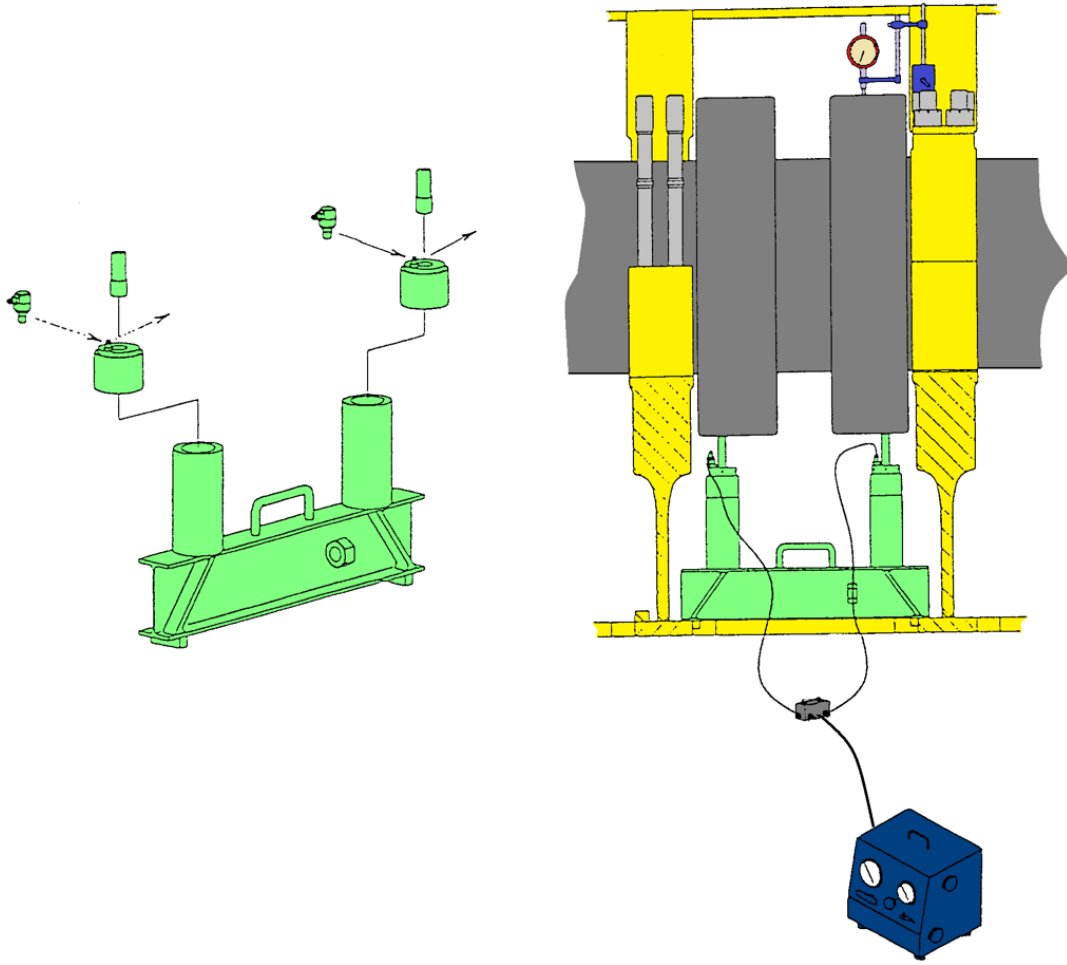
Gemi Dizel Motoru Hareketli Parçalarının Sökümü
